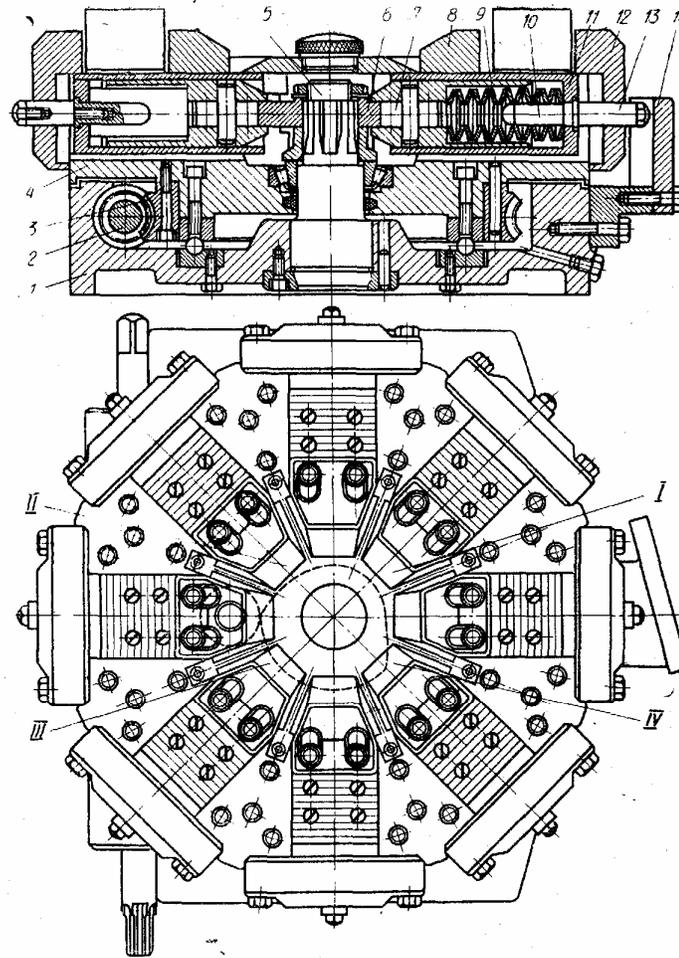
Приспособление для непрерывного фрезерования
